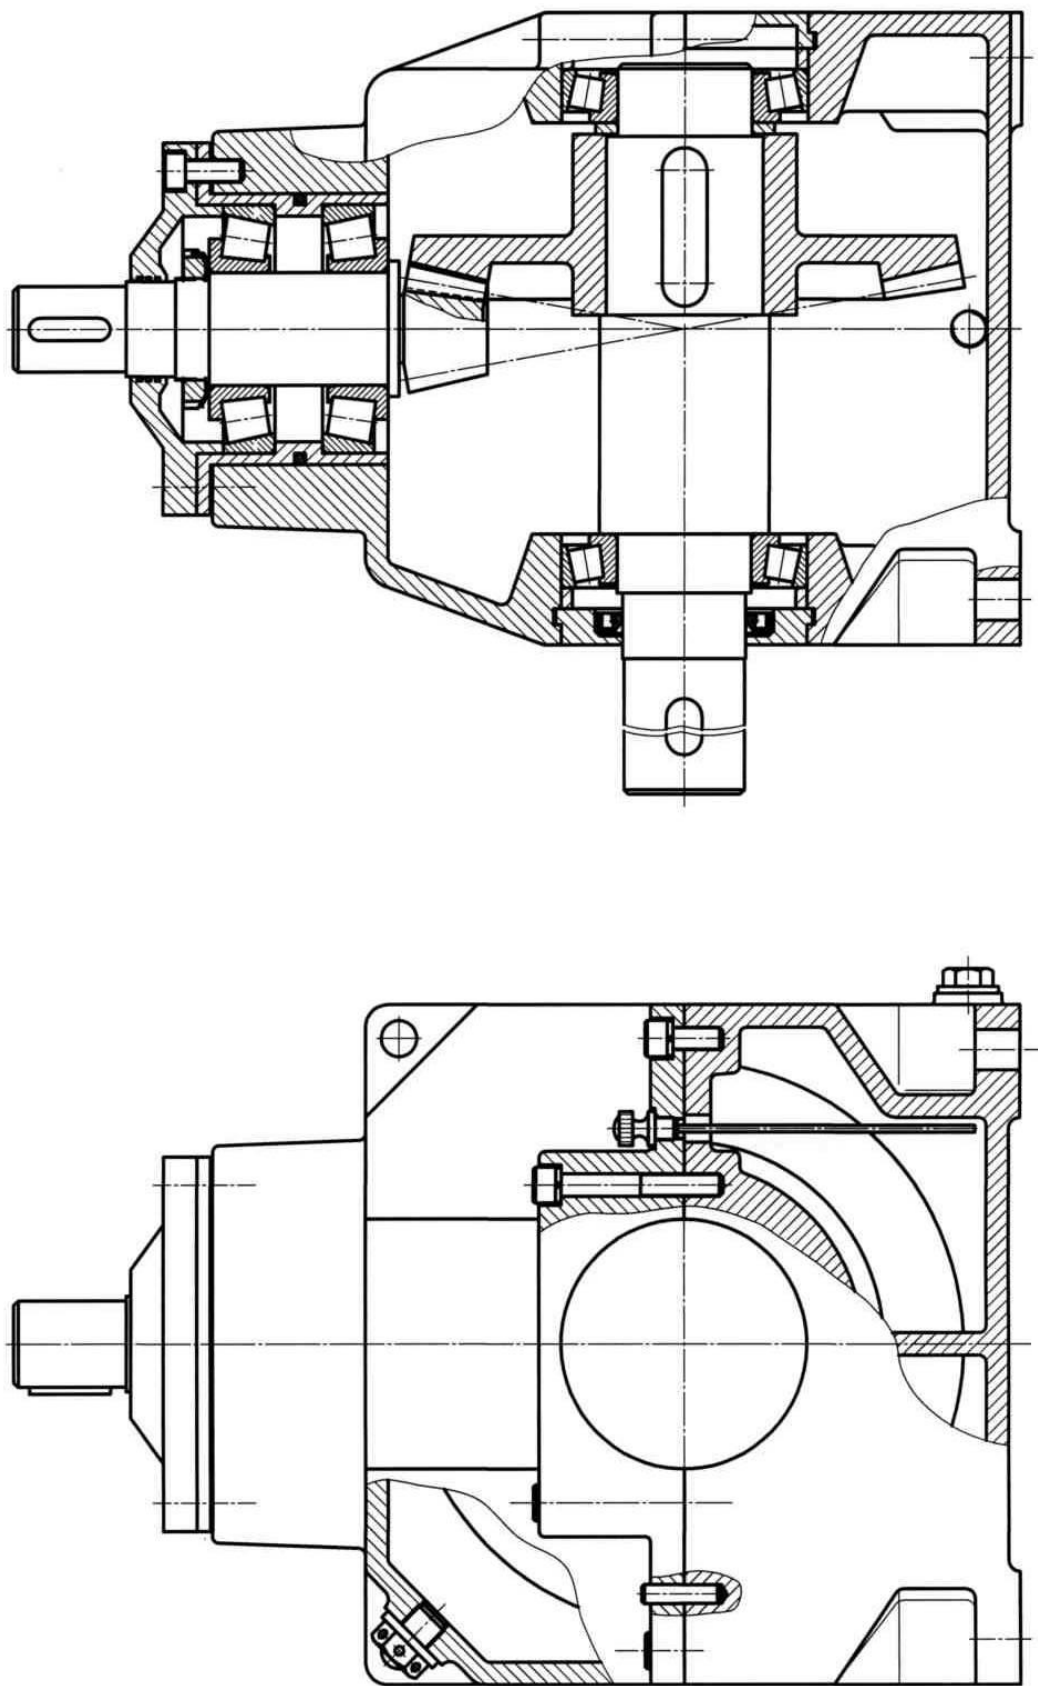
Редуктор конический с вертикальным быстроходным валом
